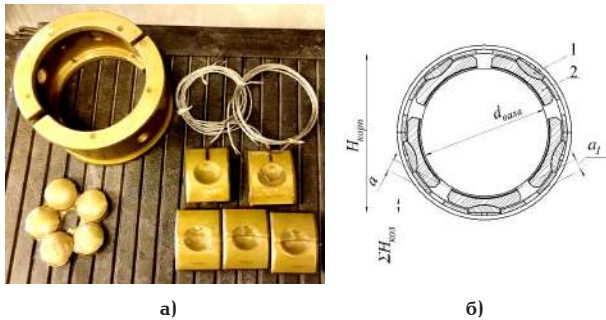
Опорный подшипник со сферической опорой: перед 3D-сканированием (а) и в процессе проведения инструментальных замеров (б)
